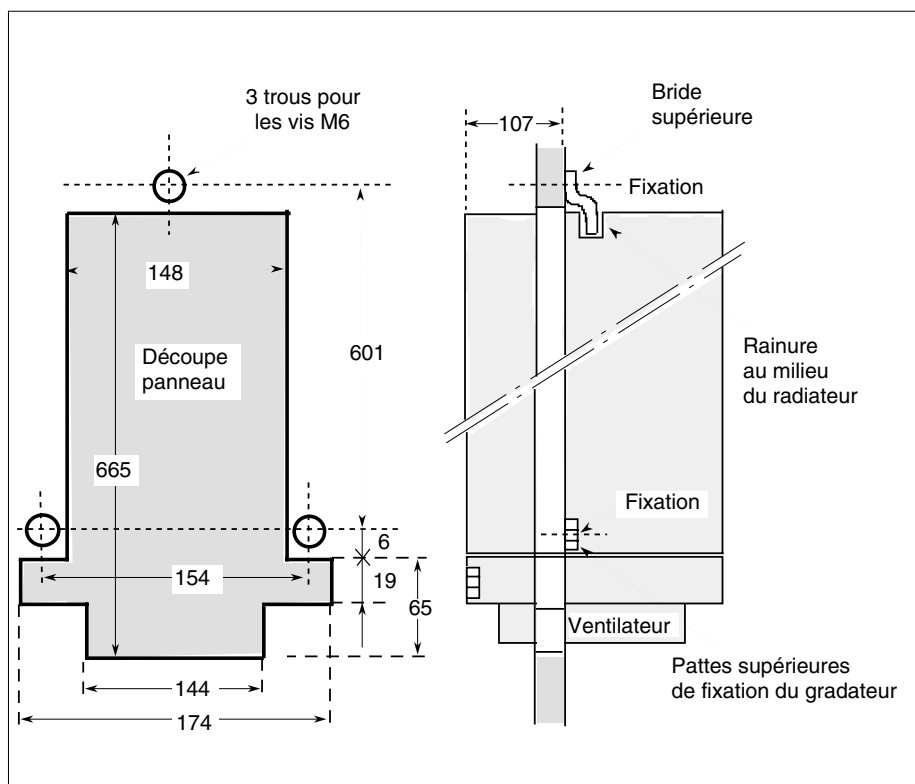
Cotes (en mm) de perçage, découpe et fixation du gradateur TU1470
